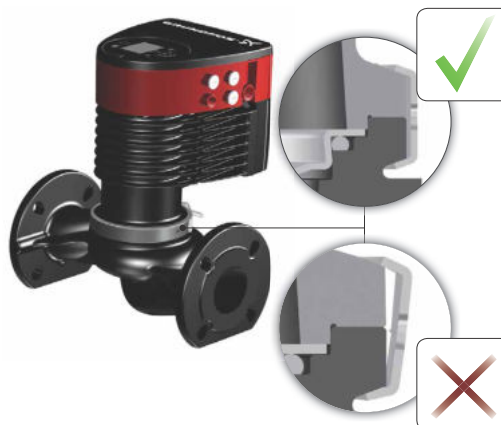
Montieren des Pumpenkopfs auf dem Pumpengehäuse
